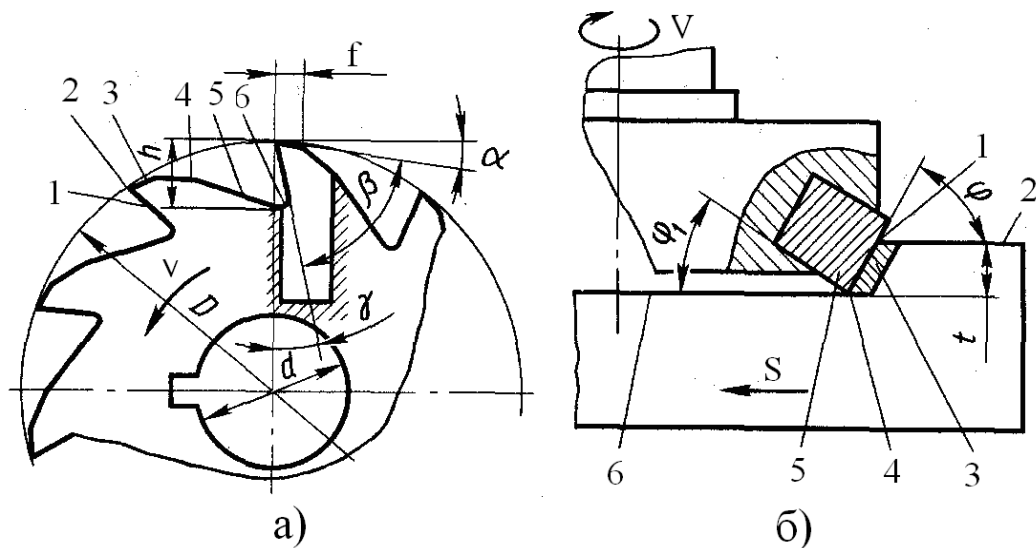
Зуб фрези: а – циліндричної; б - торцевої
